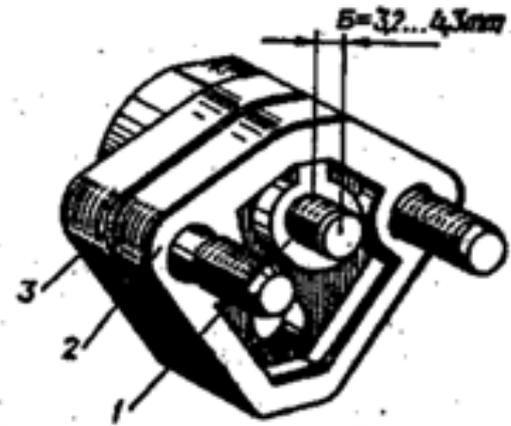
Выступающие штанги привода бензинового насоса: 1 - штанга; 2 - прокладка; 3 - уплотнительно-регулирующие прокладки; Б - расстояние от пяты рычага бензинового насоса в положении начала полезного хода до привалочной плоскости корпуса бензинового насоса
